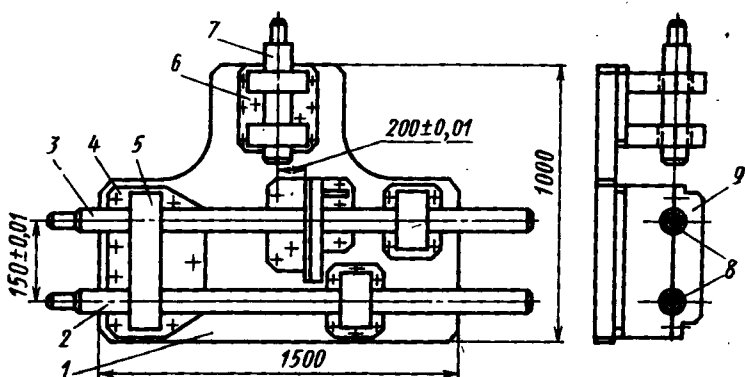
Схема приспособления для растачивания отверстий в корпусах
